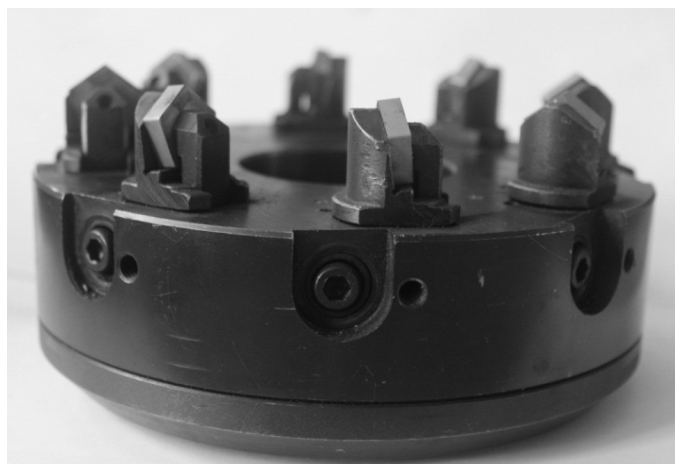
Базовый вариант блочно-модульной торцовой фрезы
